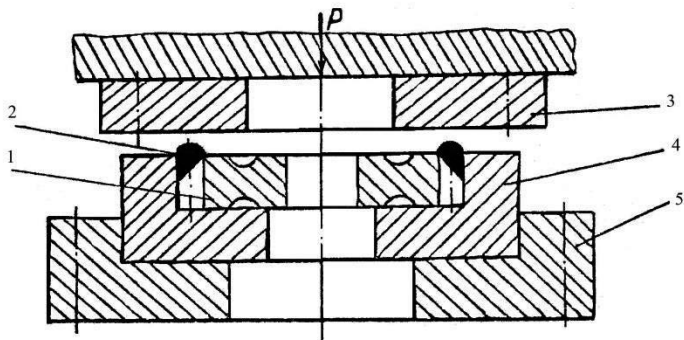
Схема опресування наплавленого зубчастого вінця:
